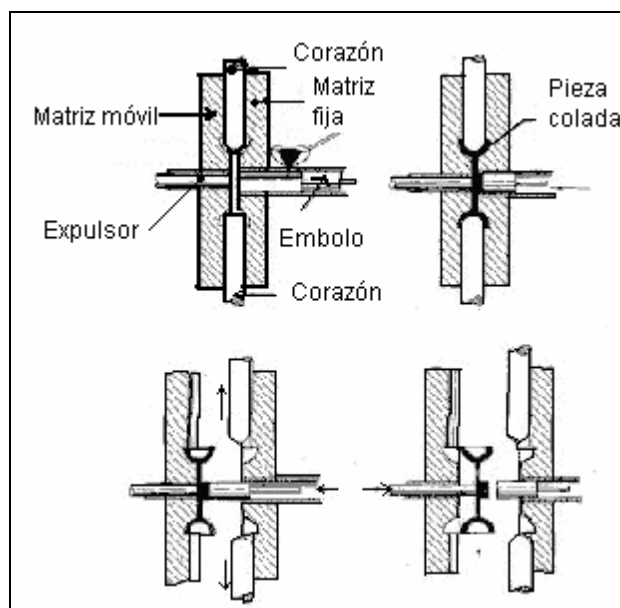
Máquina de cámara fría con émbolo horizontal
